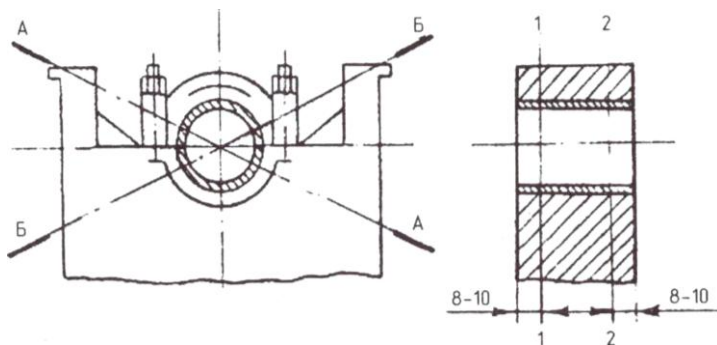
Схема измерения диаметров посадочных мест и вкладышей коренных подшипников ДВС
